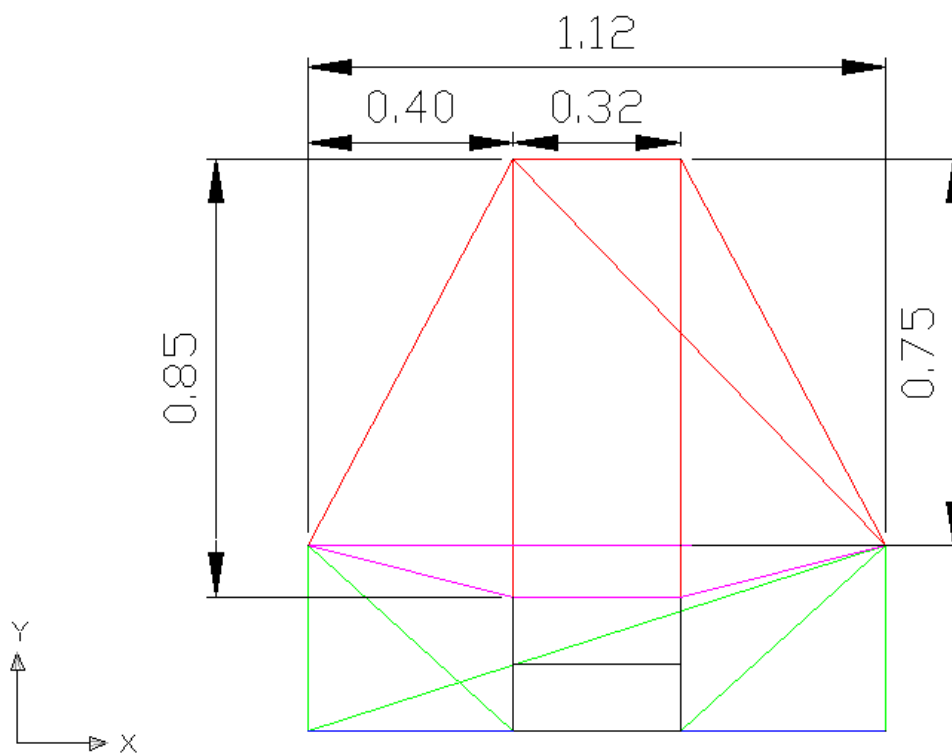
Dimensiones del ROLL BAR con Vista Frontal del Auto.
